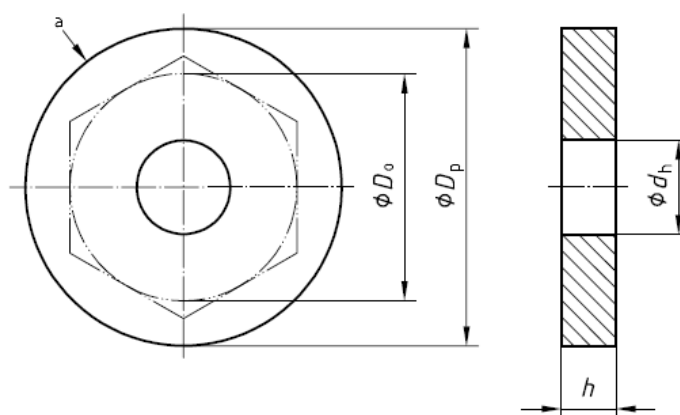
Dimensões principais da arruela ou superfície de aperto de teste [norma ISO 16047:2005]
